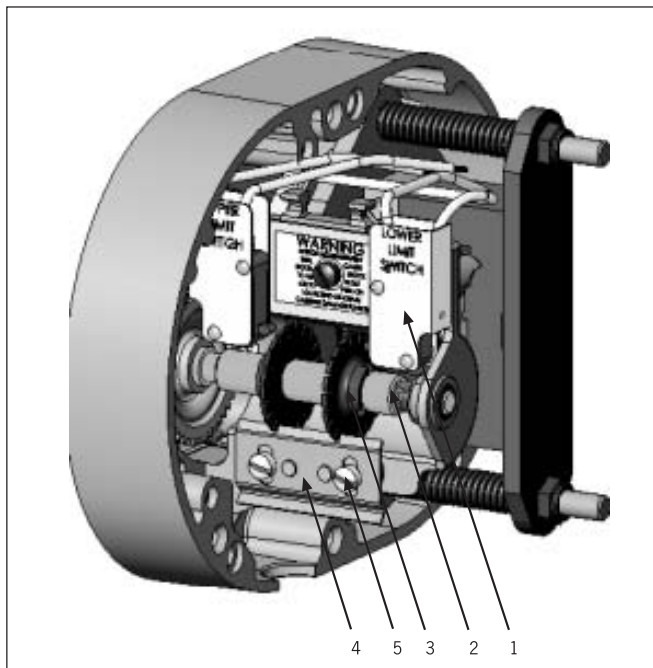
Endschalter - Gehäusetypen A bis H-2
